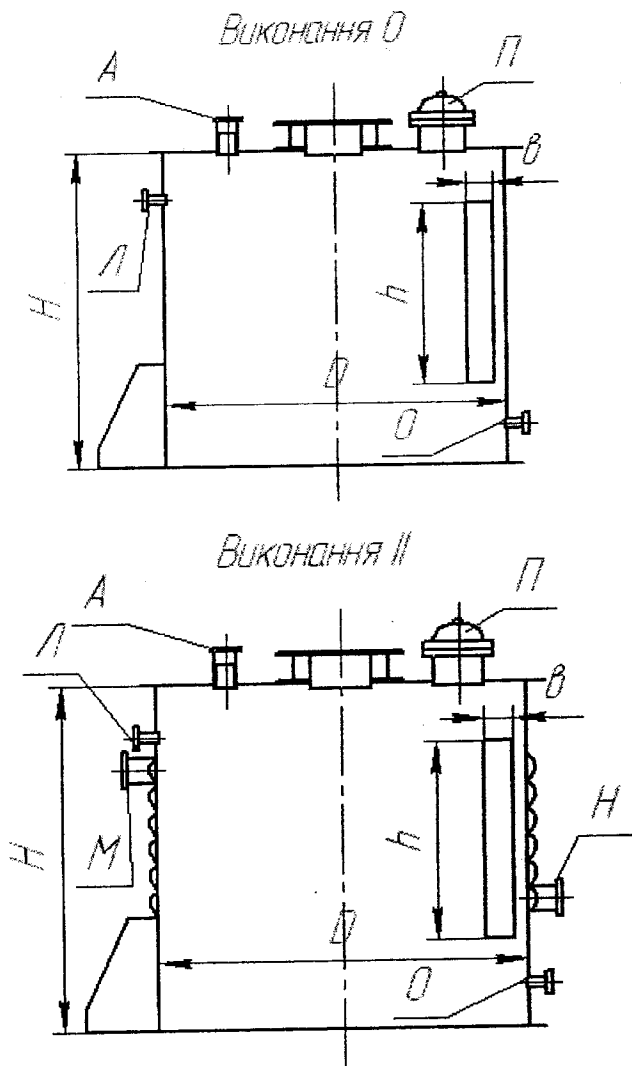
Корпуси типу 5 з приварною кришкою
